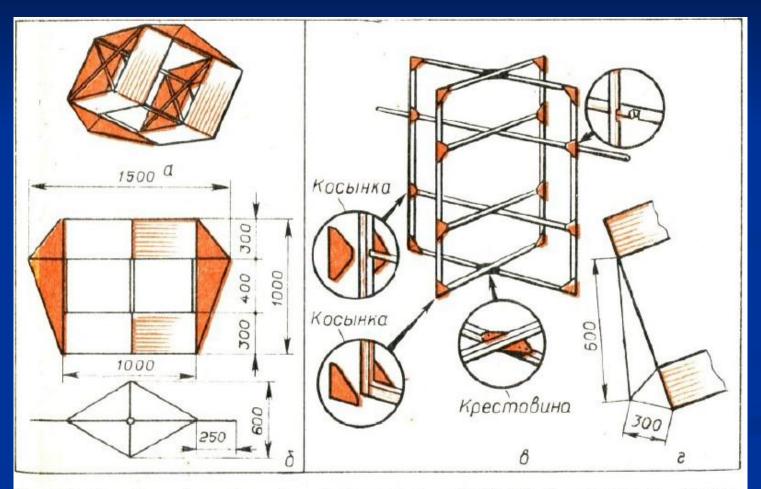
Неразборный коробчатый змей Поттера: a — общий вид; b — чертеж; b — каркас змея в собранном виде; c — размеры уздечки.
